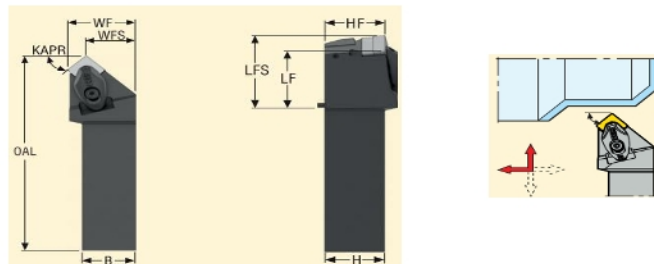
Державка DSSNR/L2525X12JET1 [1, с. 210]
